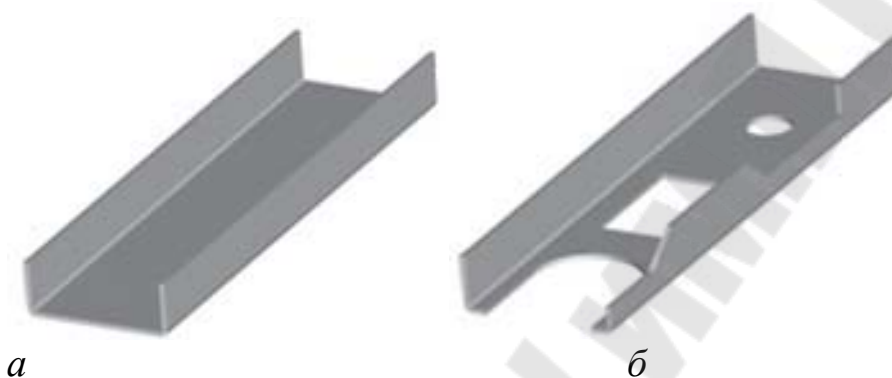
Создание базовой заготовки (*а*) и окончательный вид модели (*б*)
